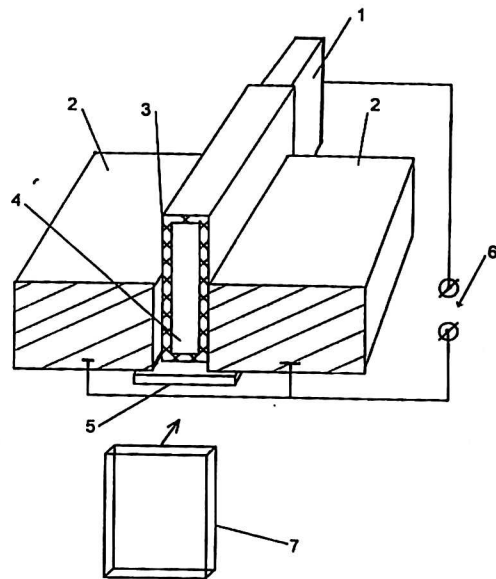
Сборка свариваемого стыка при дуговой сварке неподвижным плавящимся электродом:
